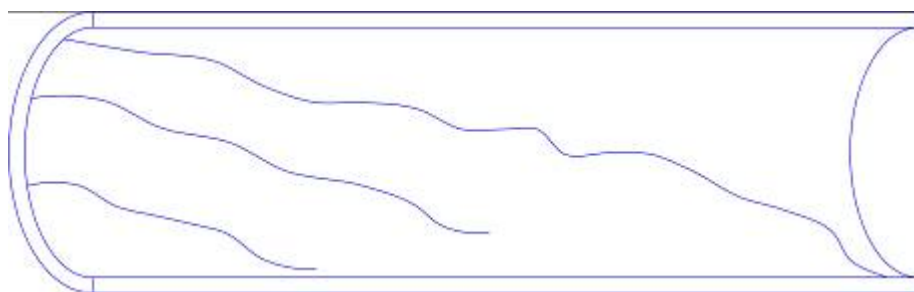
Сталеплавильные плены группового расположения на внутренней поверхности, образующиеся при раскатывании загрязненности слитка и заготовки (см. рисунок А.5, приложение А)
